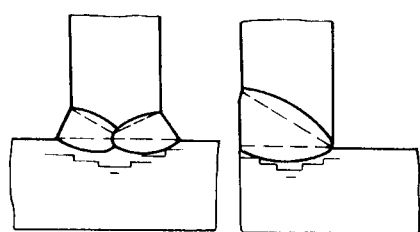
焊接接头的层状撕裂形态特征
